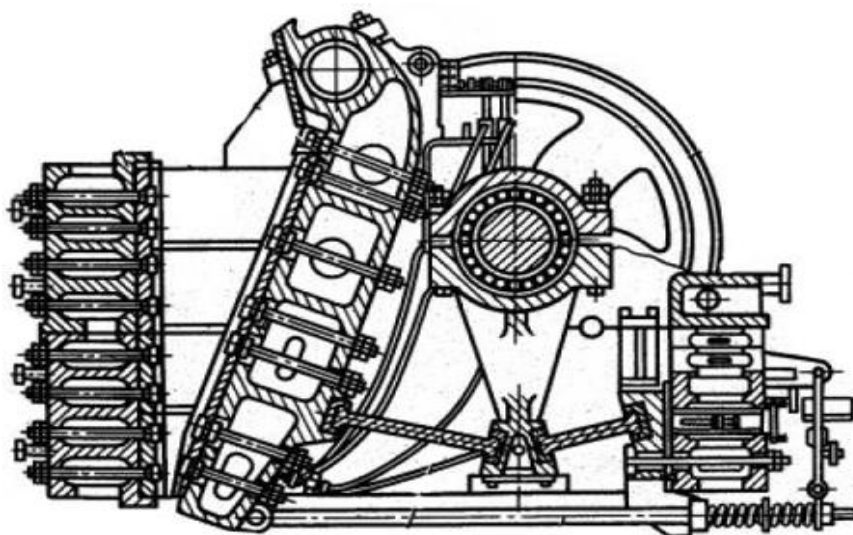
Конструкция щековой дробилки СМД-111 [4]
